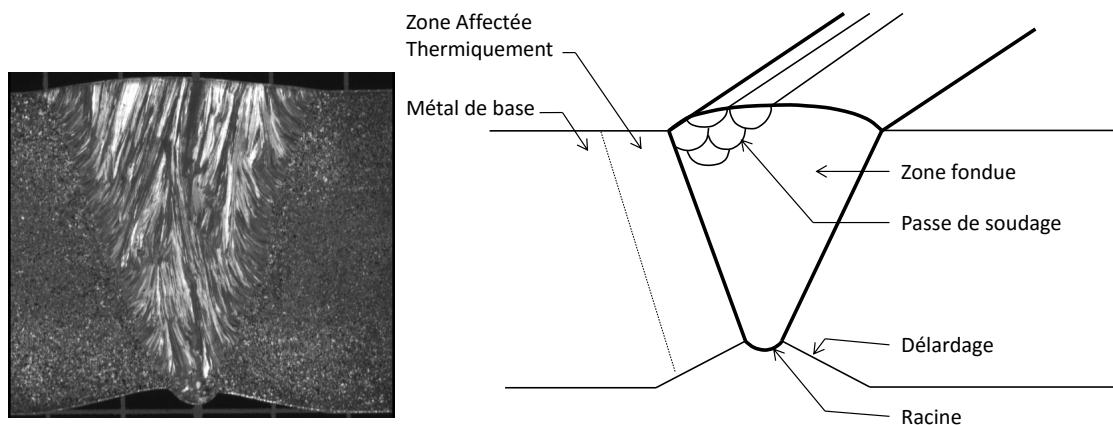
Macrographie d'une soudure multipasse EE (soudure D717C, [Cha00a]) et représentation schématique de la soudure.
